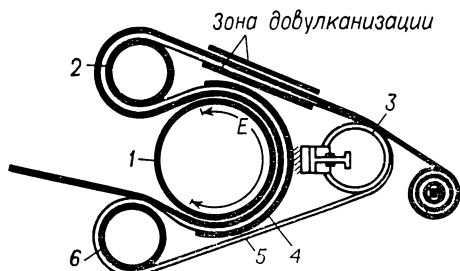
Схема барабанного вулканизатора японской фирмы «Токай-Коми»: 1 — полный барабан; 2 — верхний валок; 3 — задний валок; 4 — нагревательные элементы; 5 — стальная лента; 6 — нижний валок.
